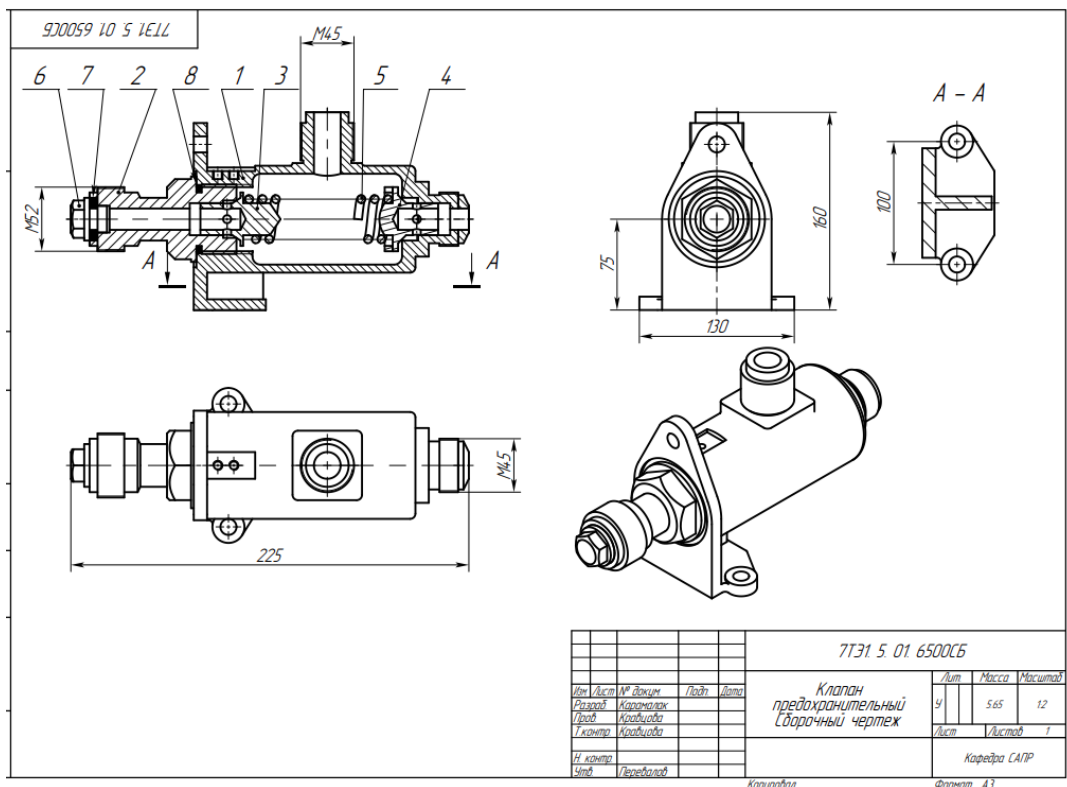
Пример оформления сборочного чертежа для задания 3
